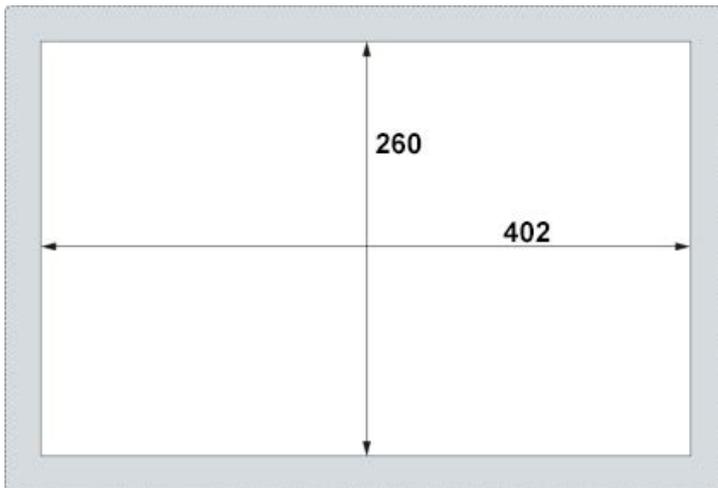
Découpe de montage GUI615 (dimensions en mm)
